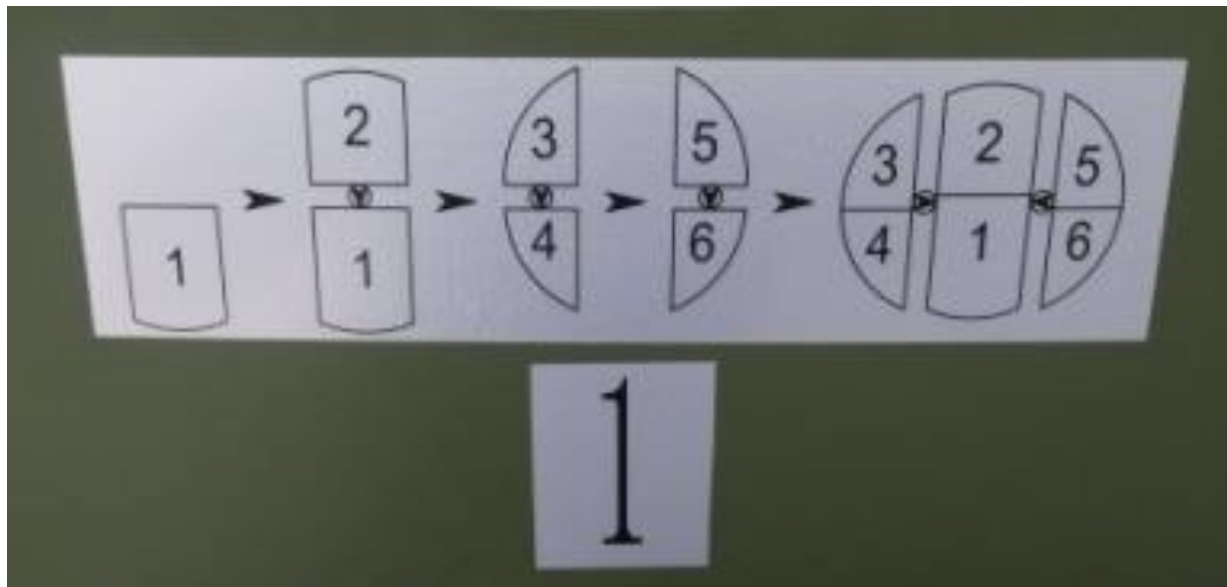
Порядок сборки рефлектора.
